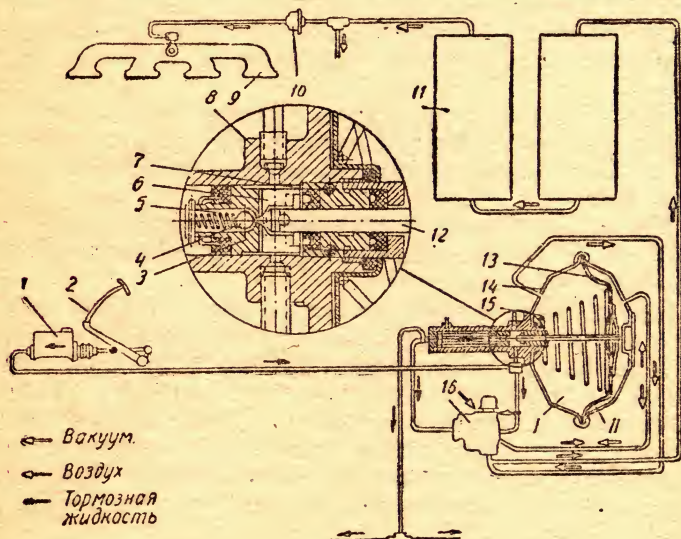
Схема привода колесных тормозов с гидровакуумным усилителем:
